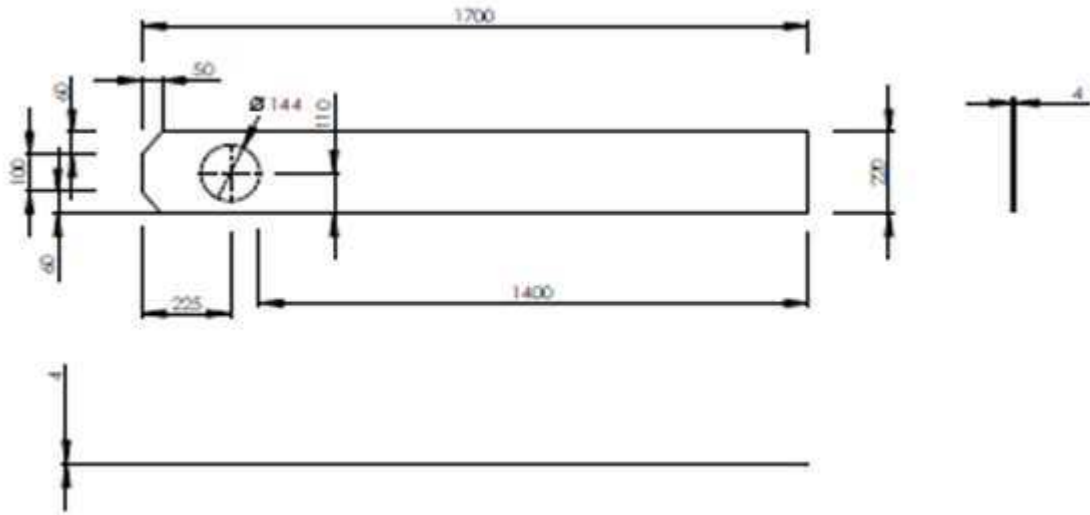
Equipamento proposto por Stepahn (2010) para o ensaio de Inderbitzen.
